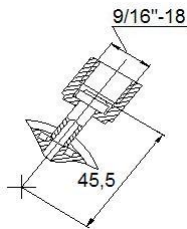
Штуцер для торцевого уплотнения Ni шайбой с гайкой с дюймовой резьбой 9/16"-18
